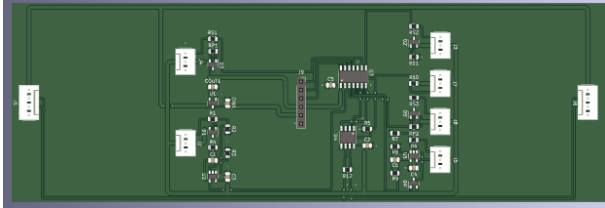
Diseño de PCB en KiCad. Fuente: Elaboración propia.
